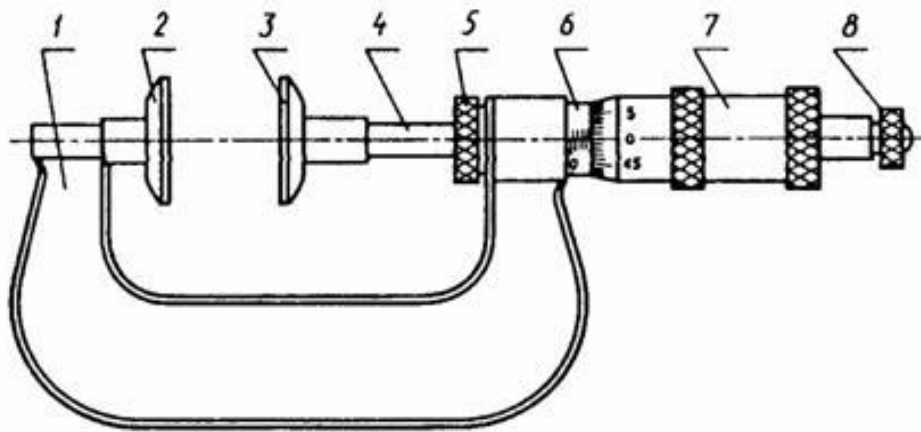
Тип МЗ. Мікрометр зубомірний: 1 - скоба; 2 – п'ята; 3 - вимірювальна губка; 4 - мікрометричний гвинт; 5 - стопор; 6 - стебло; 7 - барабан; 8 - тріскачка (фрикційна)
